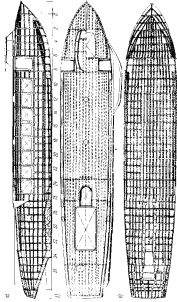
Конструктивная схема корпуса в надстройке теплохода «Белорус»: а — продольный разрез по ДП; б — план палубы; в — план днища.
